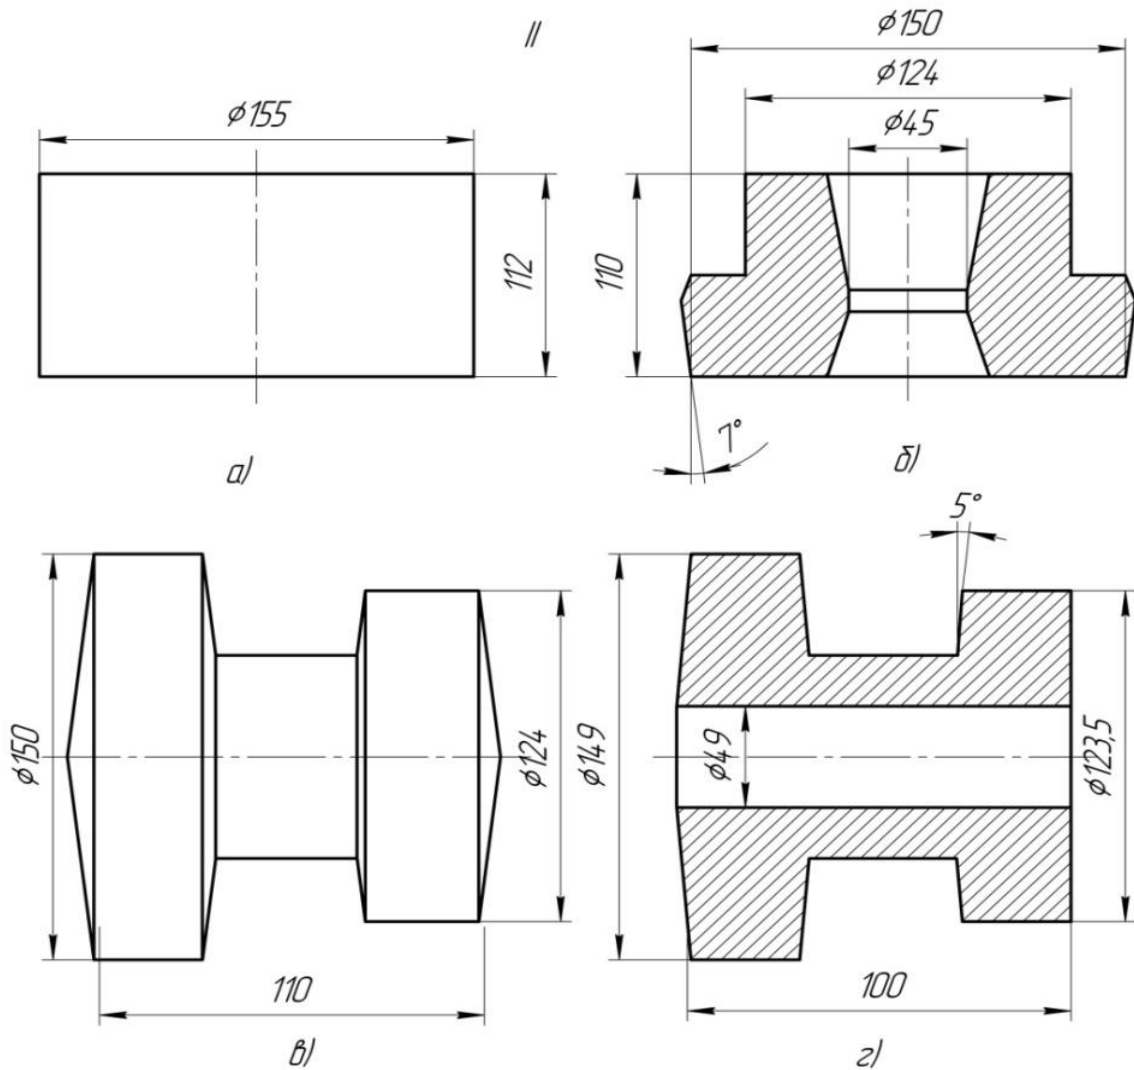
Ескізи заготовок: II – двовінцеві колеса;
